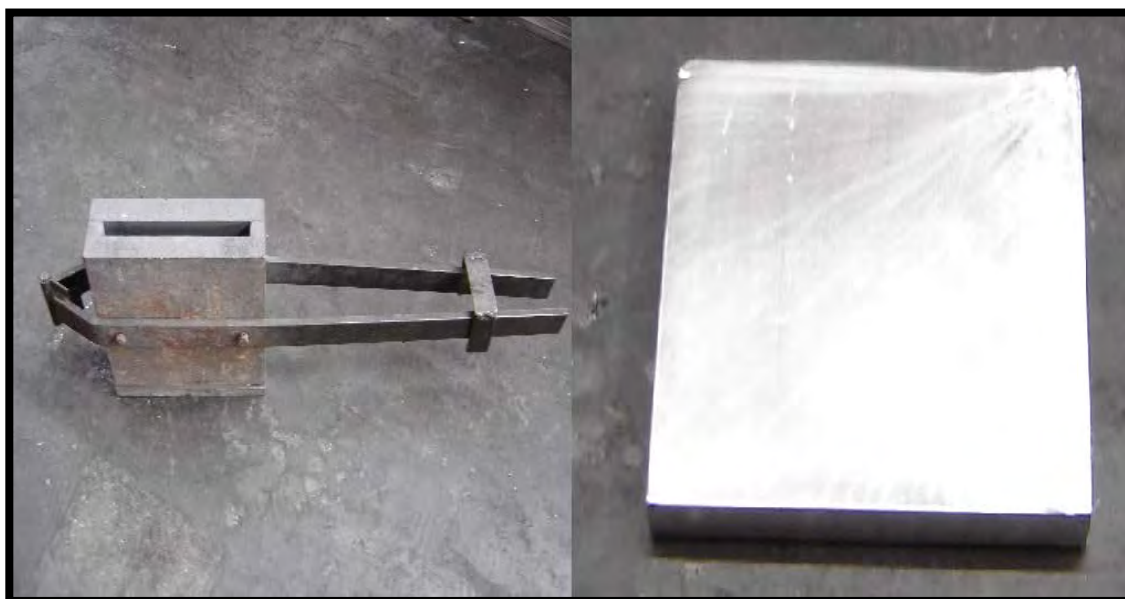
Molde de la placa de aluminio y la placa de 25 Kg de 30 mm de espesor
